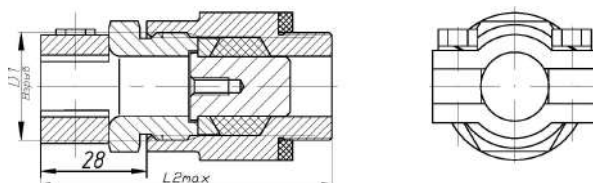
Конструкция кабельного ввода ExKV-B для прокладки бронированного кабеля. Остальное смотри рис.6.
